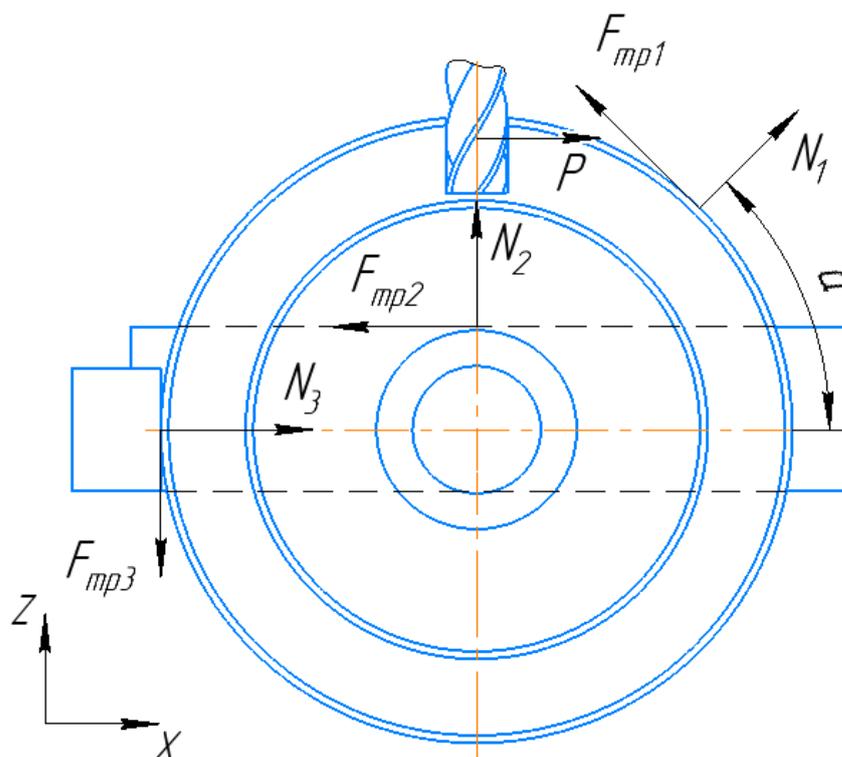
Схема сил, действующих при закреплении и обработки заготовки
